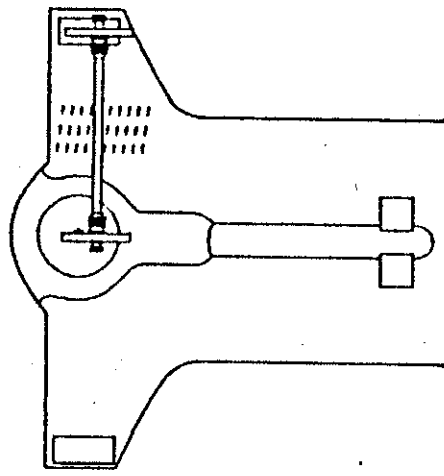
Контроль сварного соединения подкрылка скользуна с нижним листом
